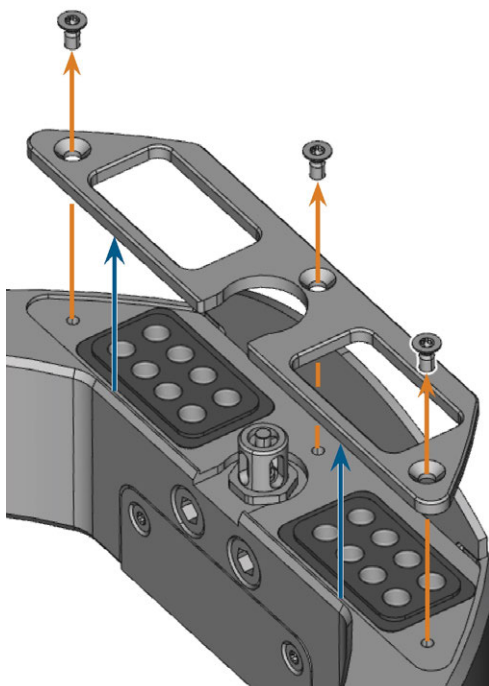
RETIRER LE COUVERCLE DU MAGASIN D'OUTILS
